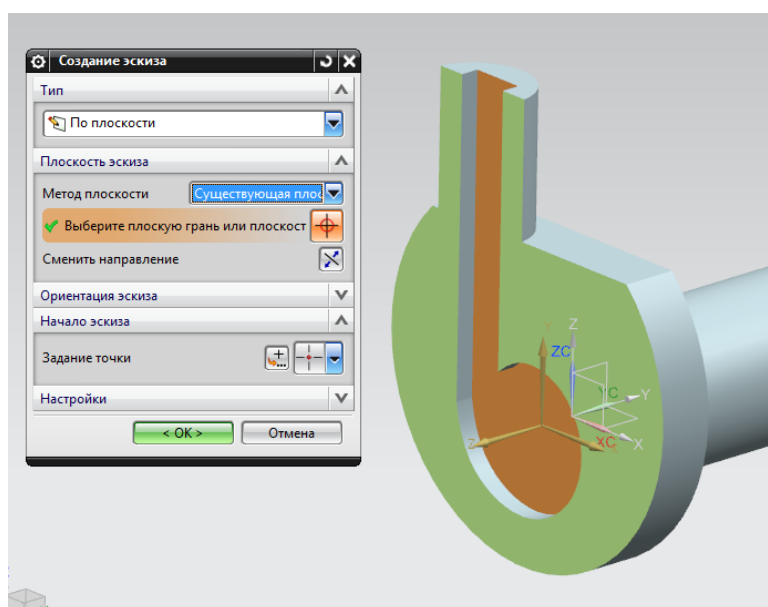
Расположение плоскости эскиза внутреннего канала трубы
